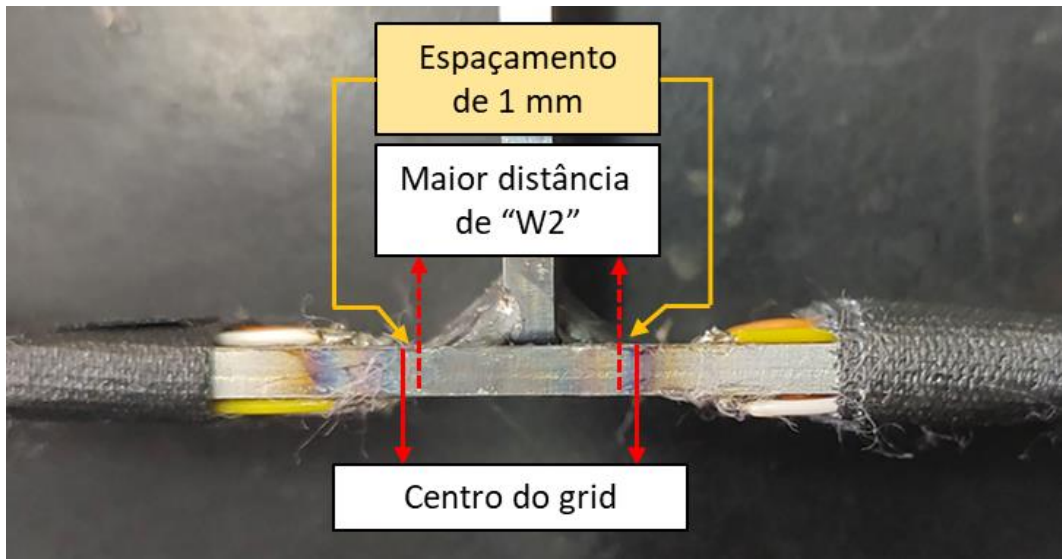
Posicionamento dos SGs no CDP do metal soldado com ponto de solda
